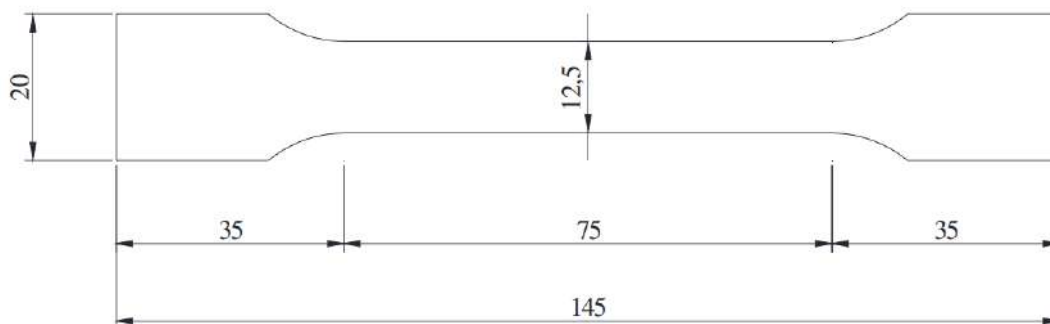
Dimensões dos corpos de prova para ensaio de tração direta (em milímetros).
